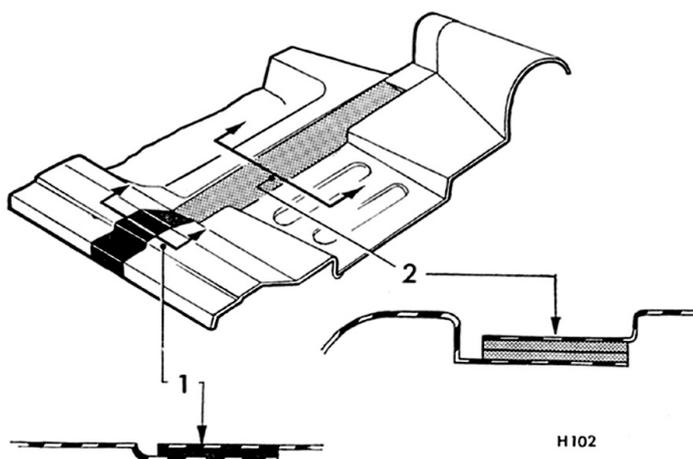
Positionnement des bandes d'étanchéité sur les panneaux de plancher
